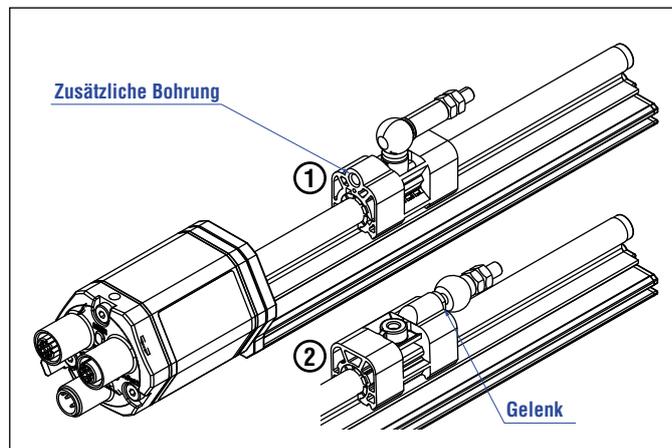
Magnetausrichtung mit Magnetschlitten für RP5 EtherNet/IP™ mit interner Linearisierung
